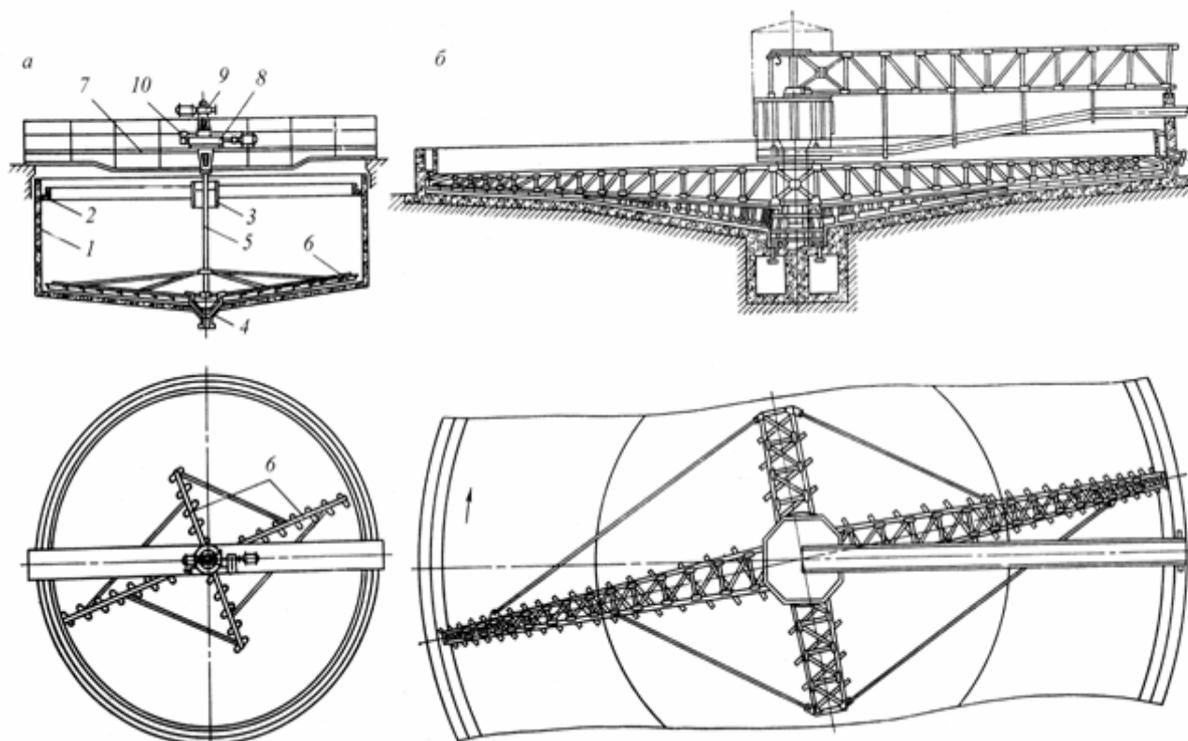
Радиальный отстойник с центральным приводом в двух исполнениях: 1 - чан; 2 - сливной желоб; 3 - загрузочная воронка; 4 - разгрузочный конус; 5 - центральный вал; 6 - граблины; 7 - ферма; 8 - привод; 9 - механизм для подъема вала с граблинами; 10 - указатель перегрузки сгустителя
